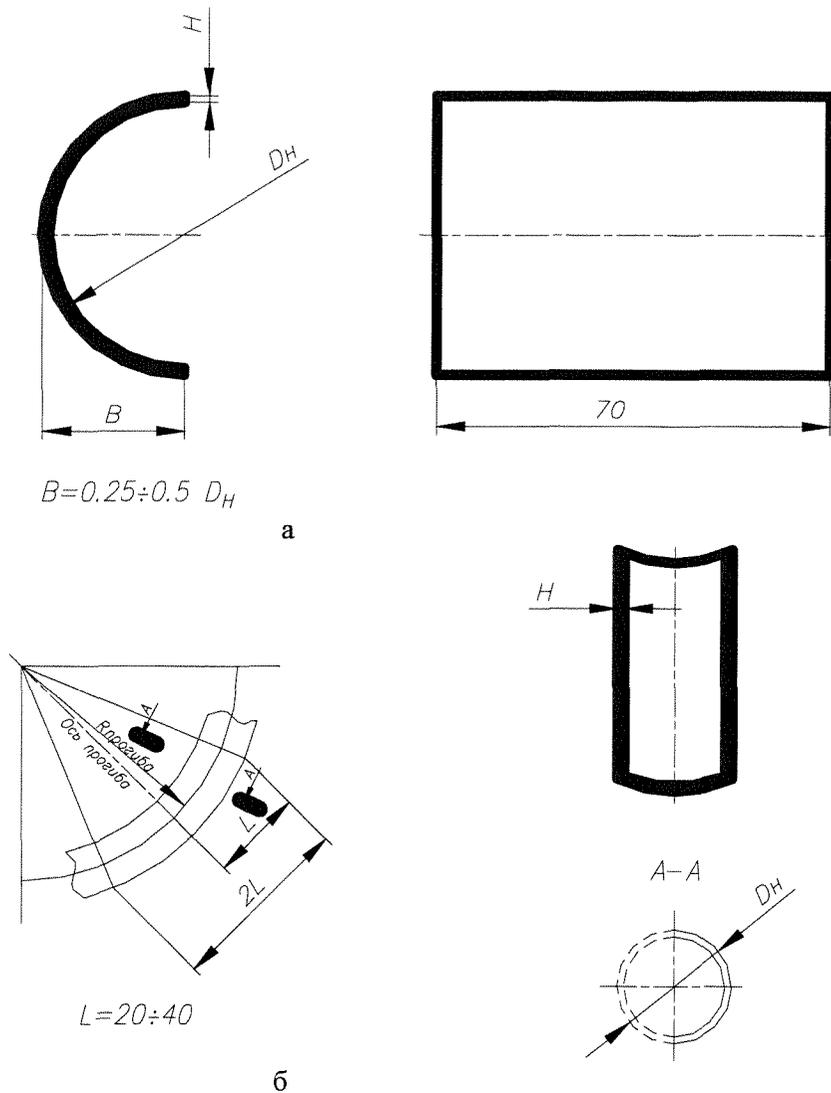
СОП в виде фрагментов изделий: а - отрезка трубы; б - участкагиба трубы
